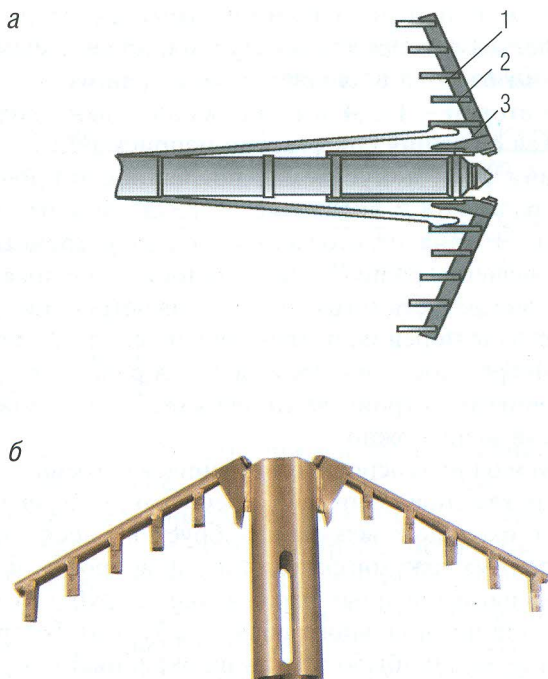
Калибровочное устройство типа «елочка» («гребенка»): а – схематическое изображение (1 – упоры, 2 – штанги, 3 – корпус); б – фотография
